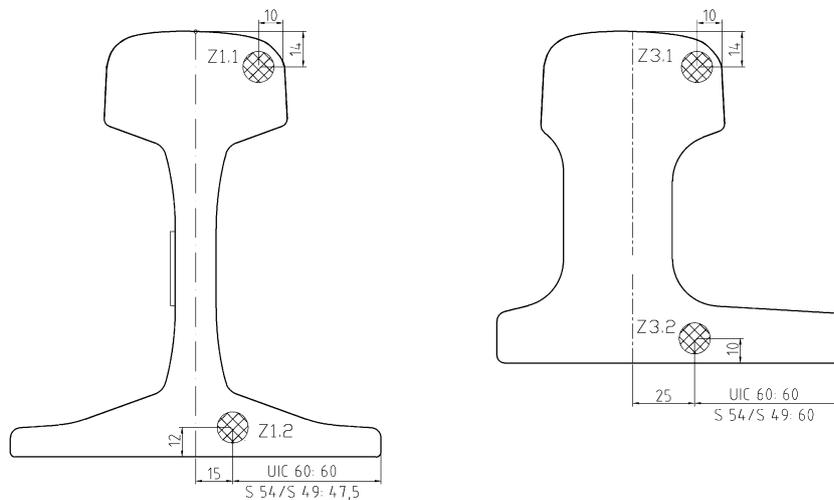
Entnahmeorte für die Zugproben Z1.1 bis Z3.2
